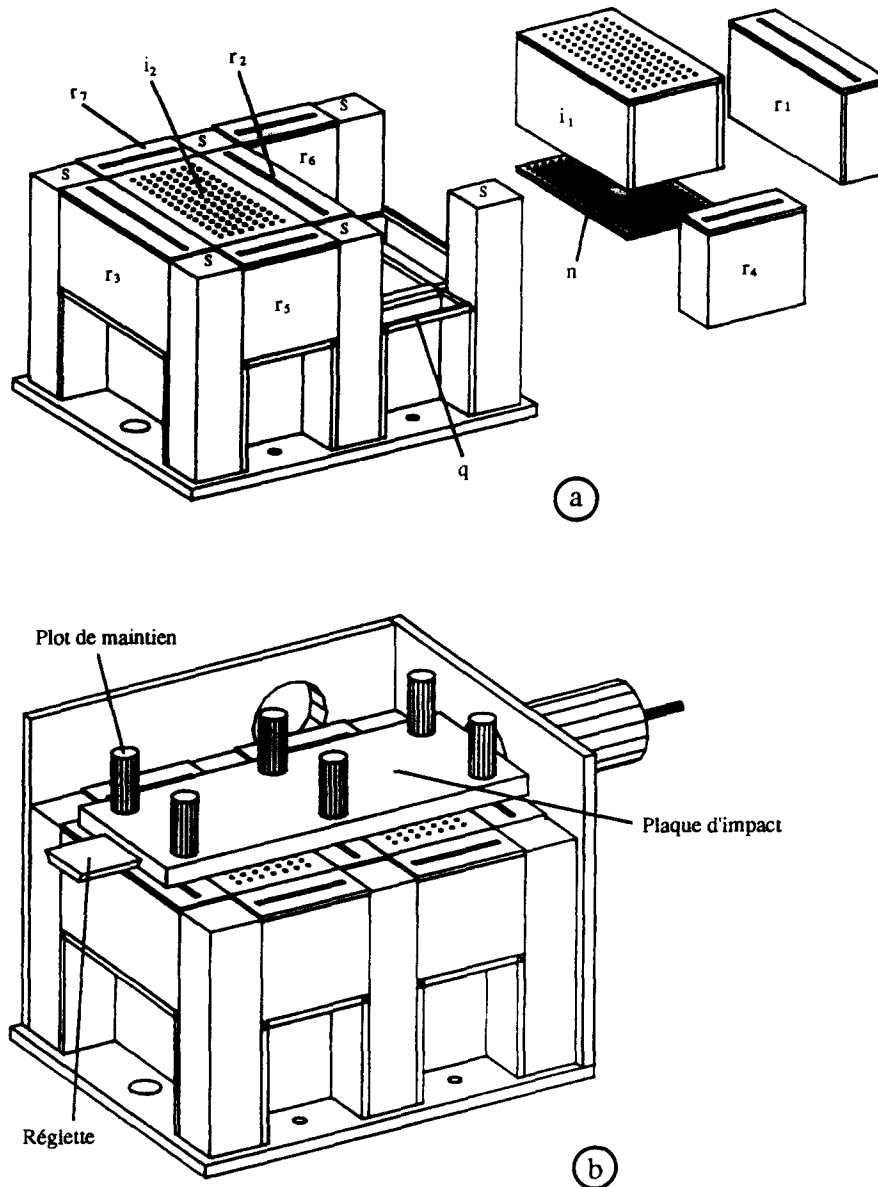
Vue d'ensemble de la maquette : (a) éclatée et (b) avec plaque d'impact.
